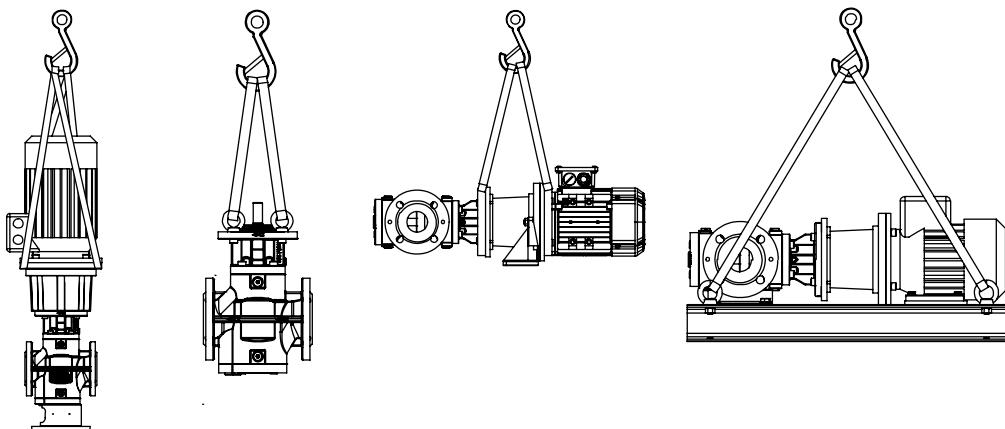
Befestigung Hebezeug - Prinzipbilder
